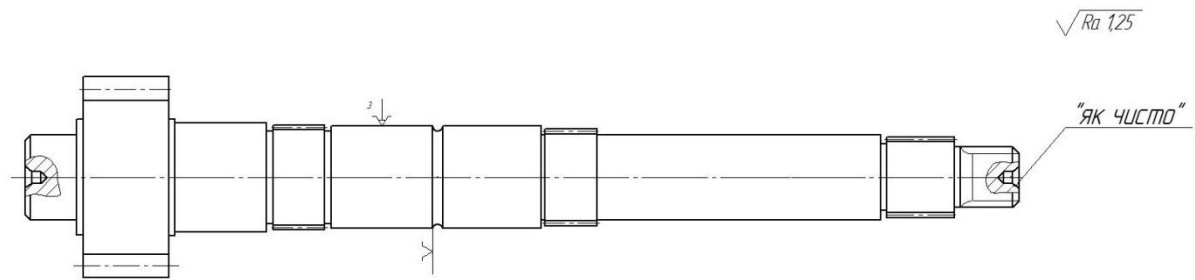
Схема базування вала на етапі токарного оброблення
